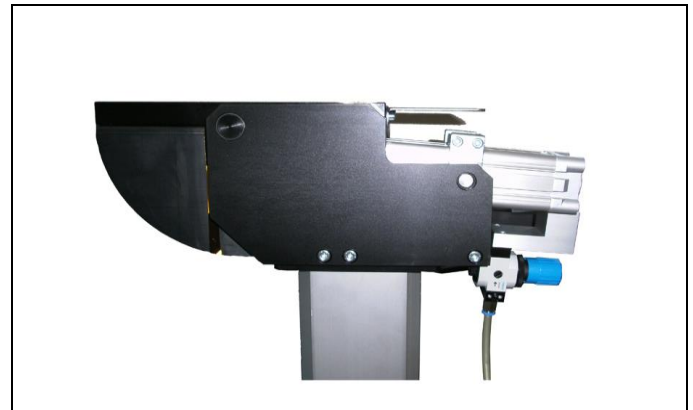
Art der Befestigung, Beispiel auf einem Hubmodul
